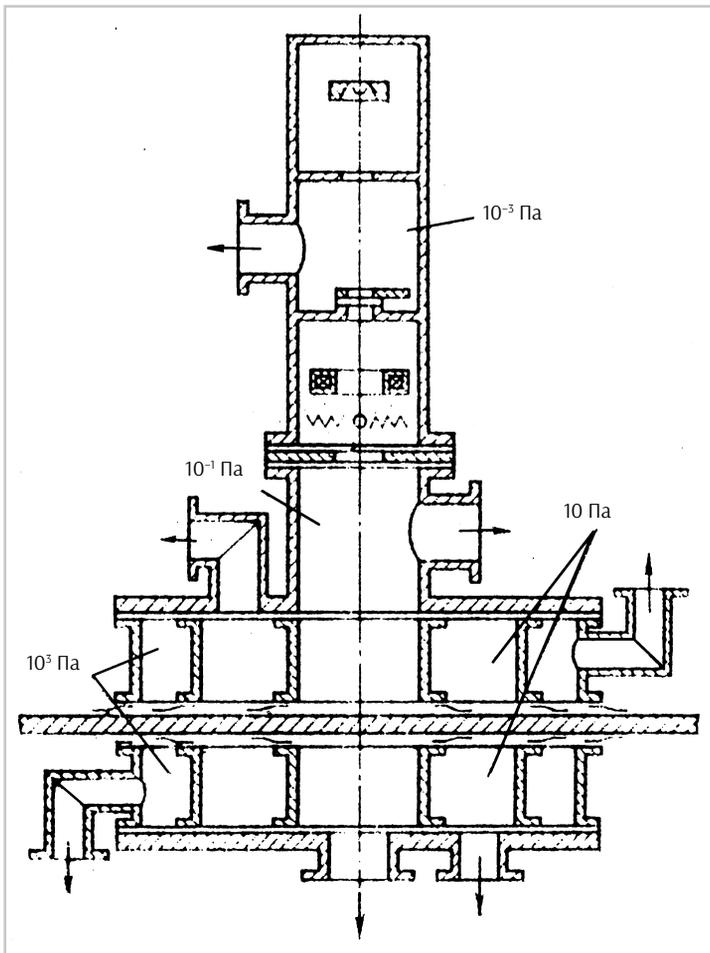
Подвижная установка для электронно-лучевой сварки с частичной герметизацией изделия
